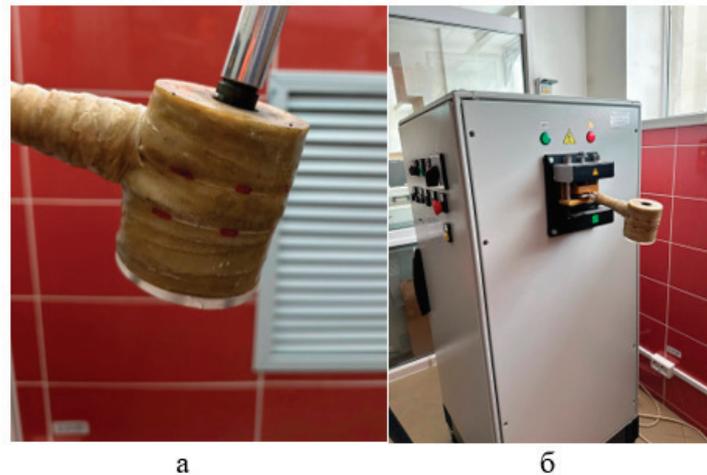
А — размещение заготовки внутри цилиндрического индуктора; б — магнитно-импульсная установка «МИУ-3»
